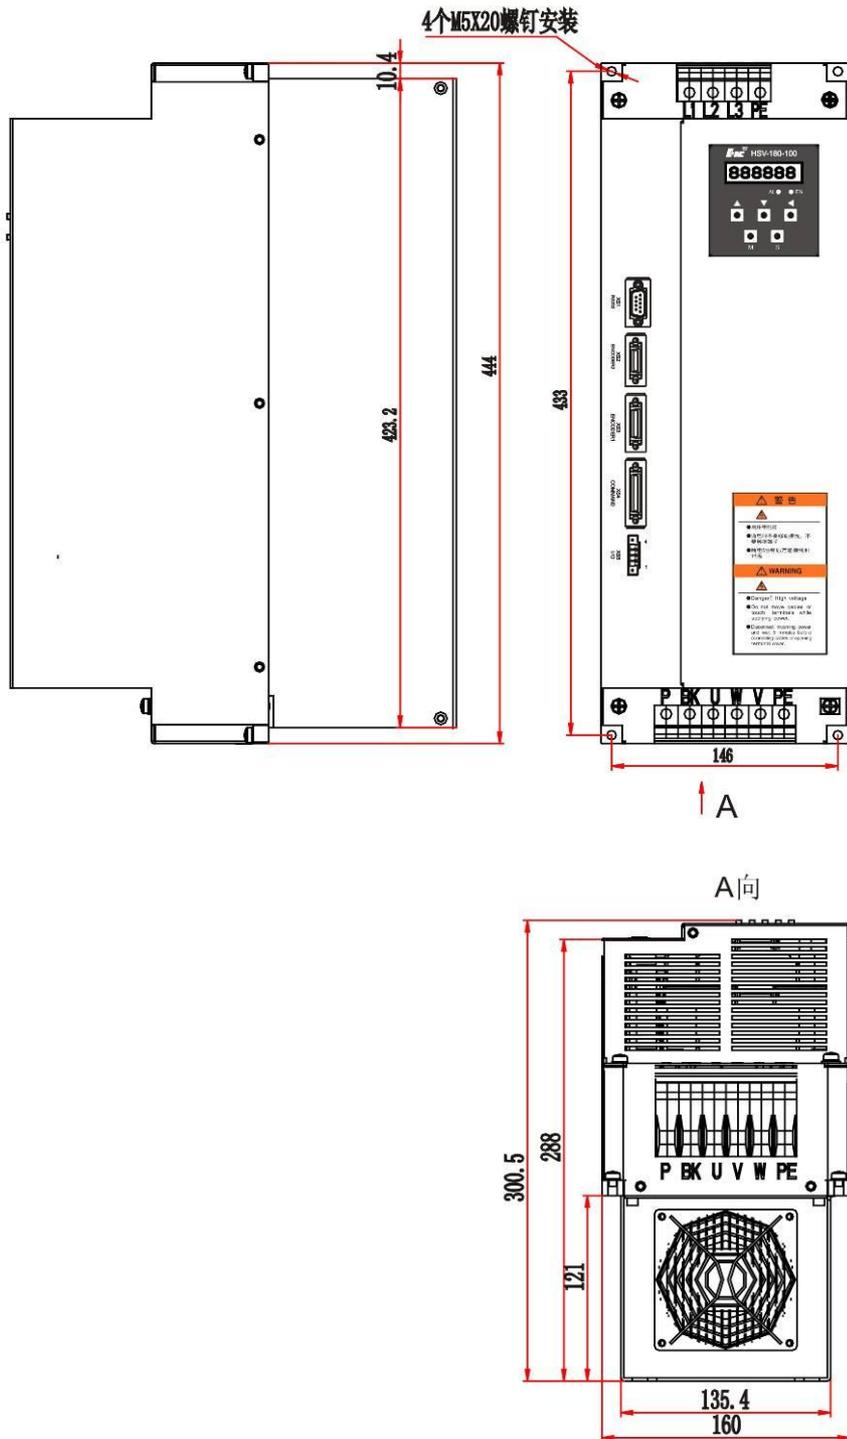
HSV-180AD-100, 150 伺服驱动单元外形尺寸 (未带辅助安装装置 单位: mm)
